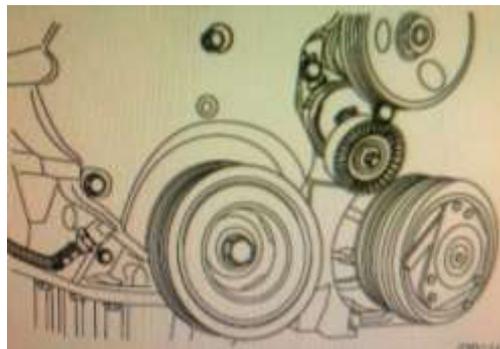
Montaje y Ajuste de Polea del Cigüeñal
